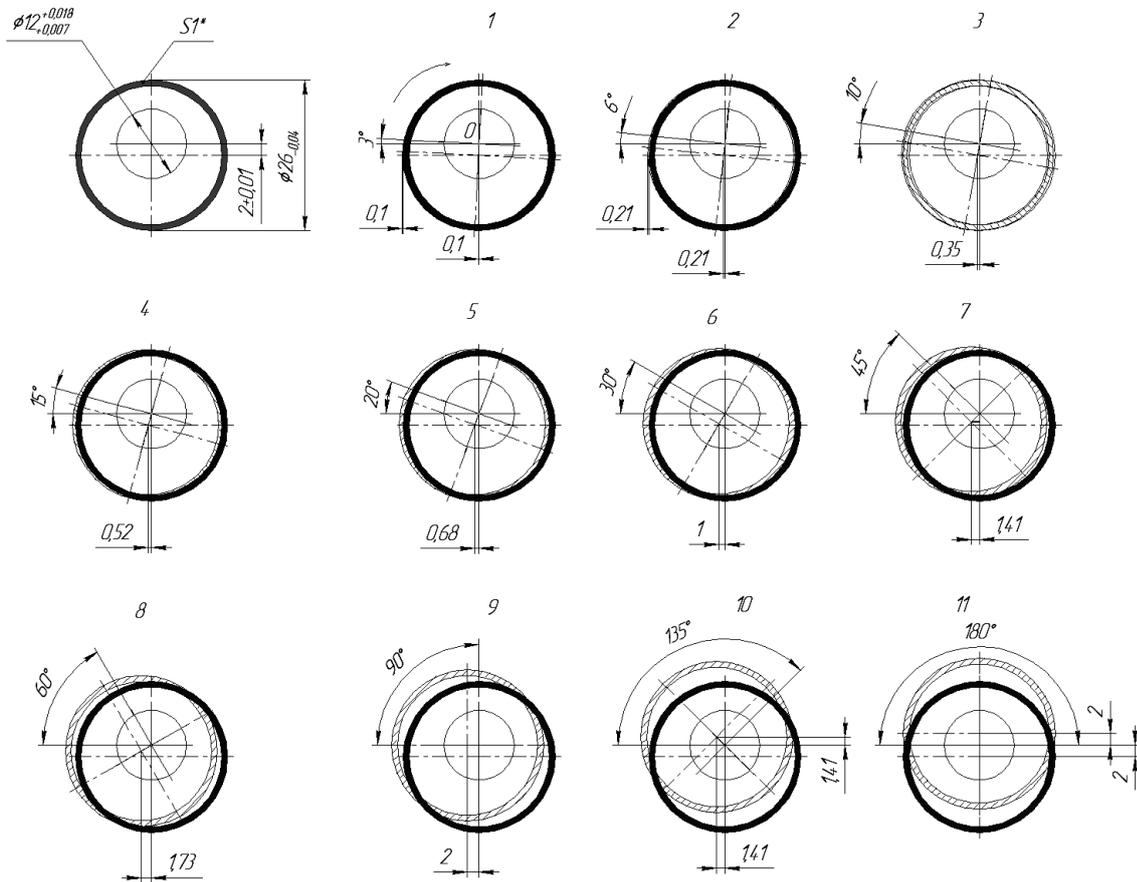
Последовательность процесса резки трубчатой заготовки одновременным сдвигом и кручением
